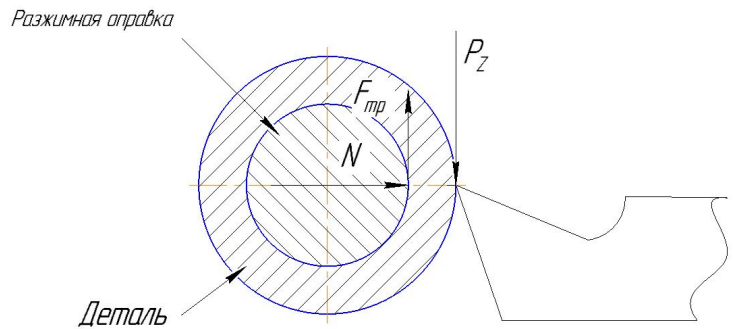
Схема сил, действующих при резании и закреплении заготовки
